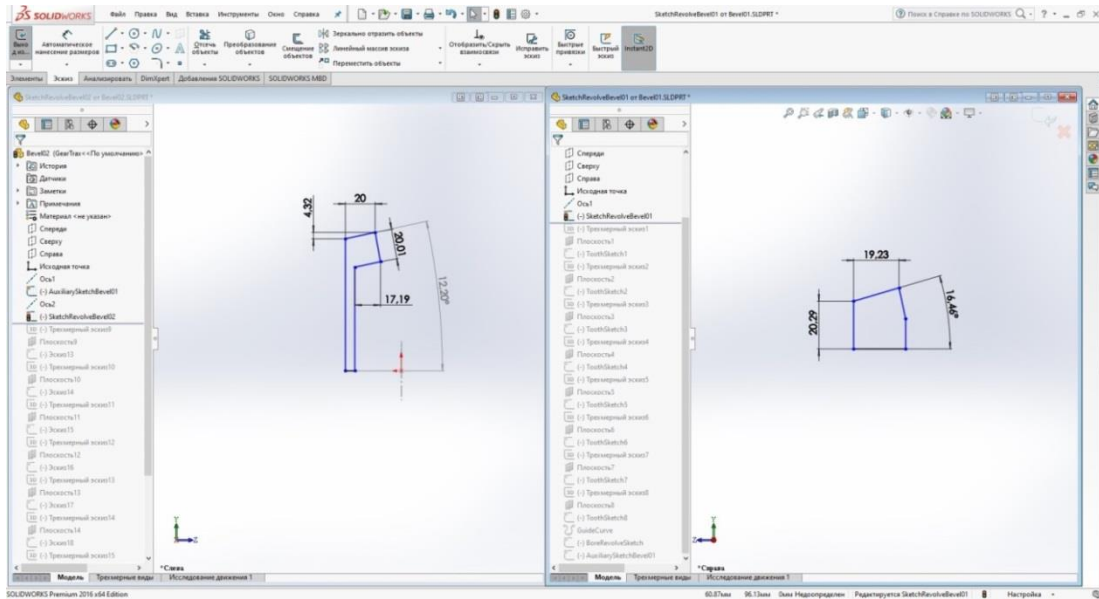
Эскизы шестерни и колеса главной передачи
